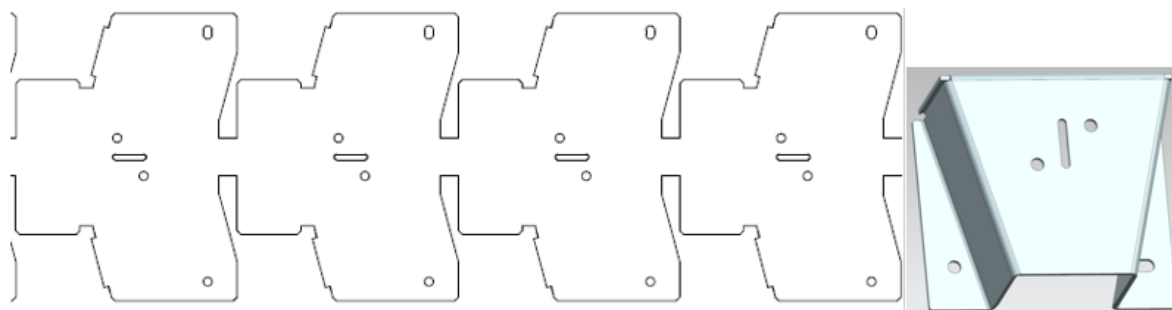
Varianta 1 – zleva výstup z prvního a druhého stroje.
